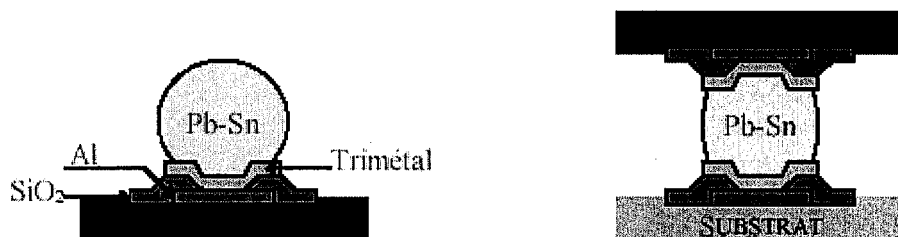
Technologie C4: Boules de soudure.
